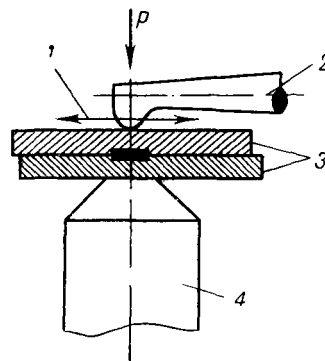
Схема ультразвуковой сварки металлов:
